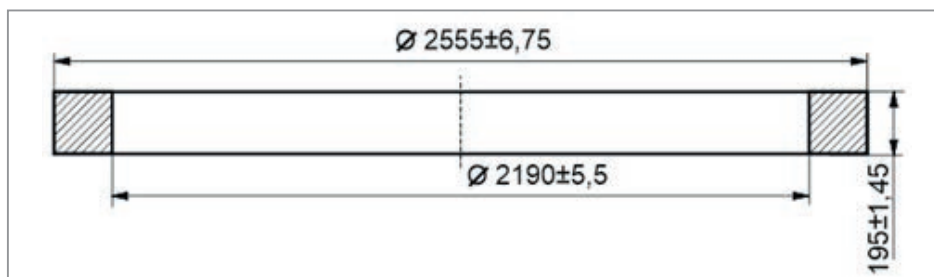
Эскиз окончательной кольцевой заготовки с прямоугольным сечением
